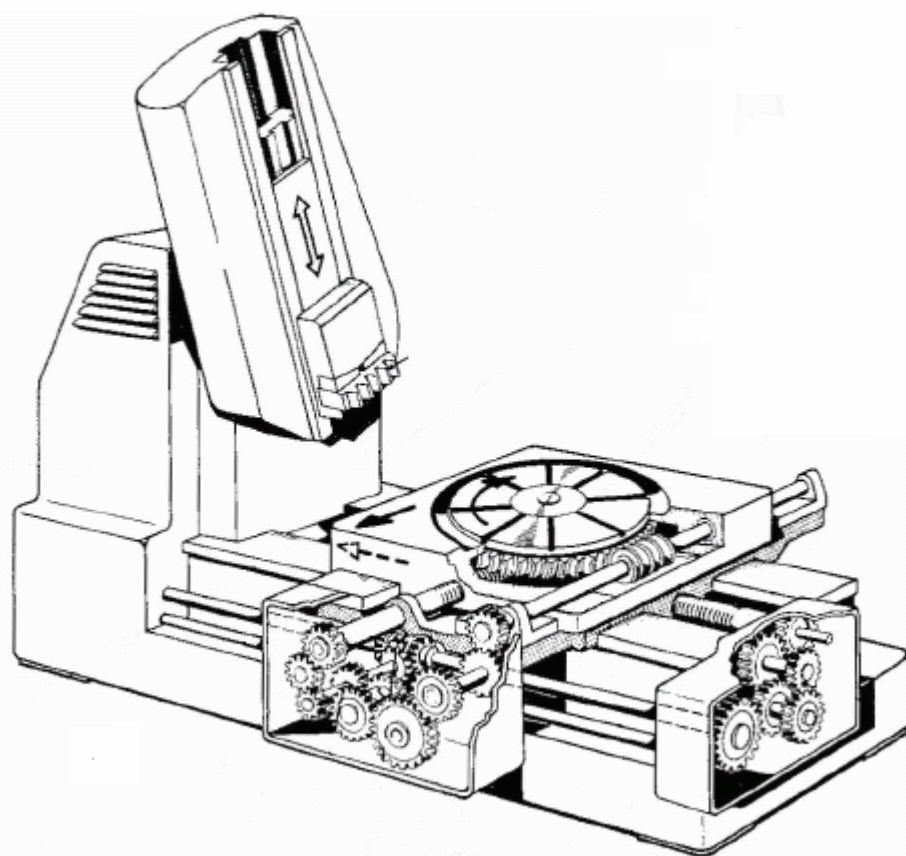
Kinematika obrázení metodou MAAG [28]
